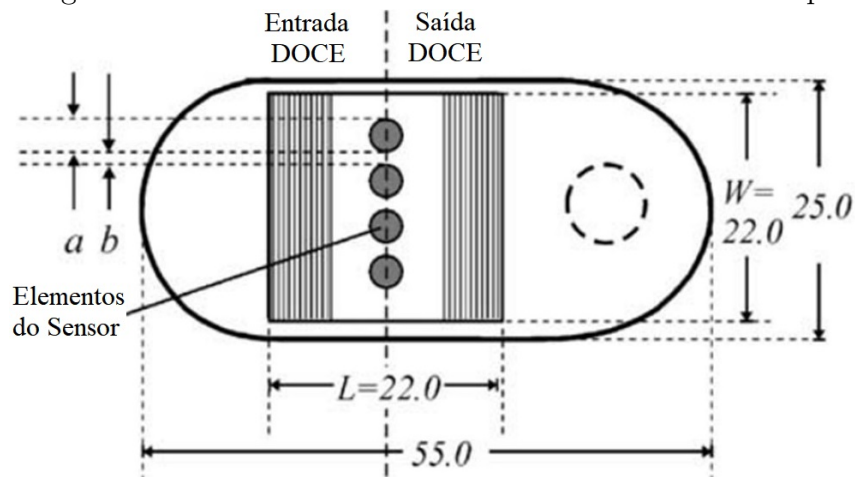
Detalhamento técnico e dimensões do Virchip.
